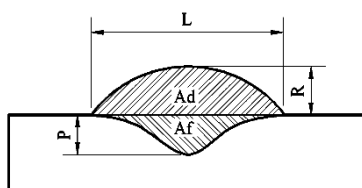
Representação esquemática das dimensões geométricas das seções transversais dos cordões de solda.
